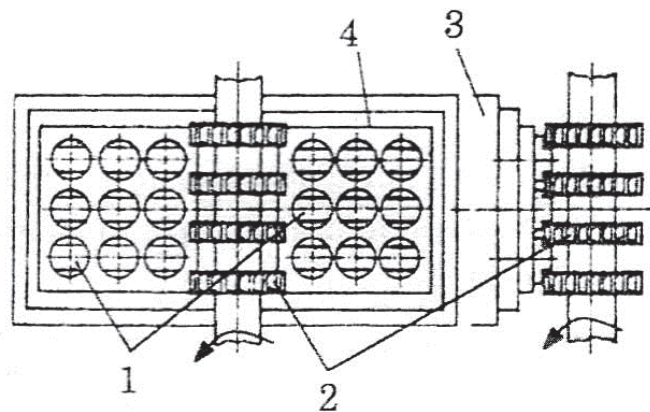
Фрезерование деталей, установленных рядами: 1 – обрабатываемые детали; 2 – набор фрез; 3 – стол станка; 4 – приспособление
